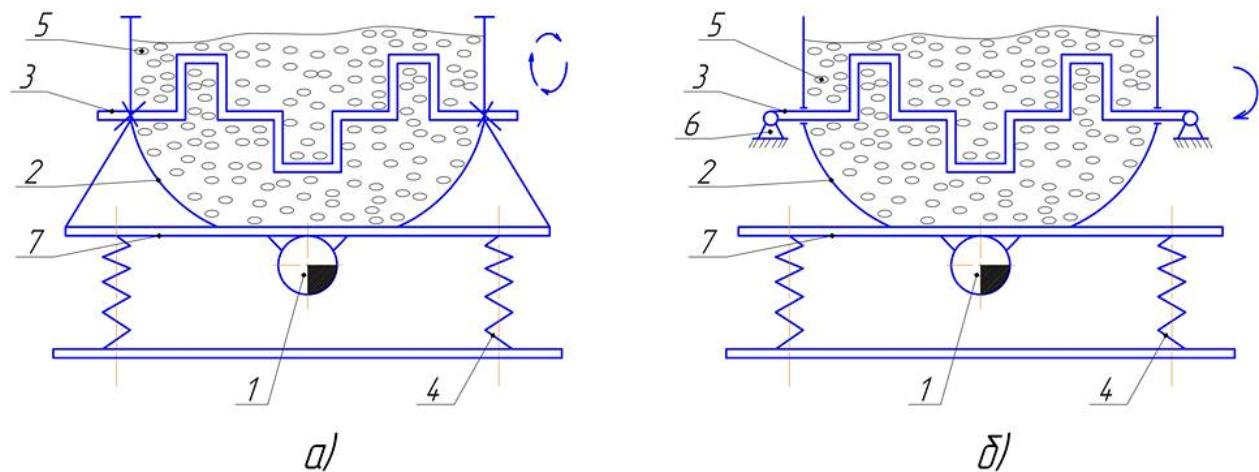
Экспериментальные схемы виброобработки коленчатых валов: а) для проведения упрочнения всей поверхности со стабилизацией напряжений; б) только для проведения упрочнения всей поверхности; 1 – вибратор; 2 - рабочая камера; 3 – деталь; 4 – пружины; 5 - рабочая среда; 6 – опоры; 7 – платформа
